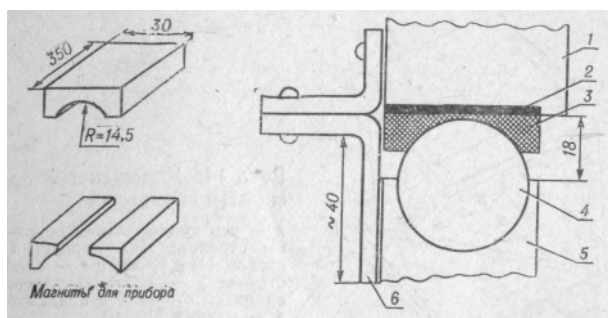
Магнитный прибор контроля (ортоскоп) наводки пневматической винтовки ИЖ-38 (ИЖ-22):
